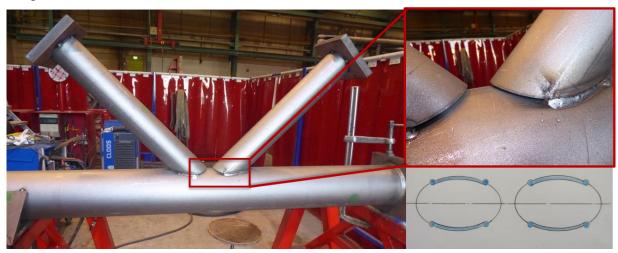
Heftschweißung bei kleinen KHP K-Knoten
